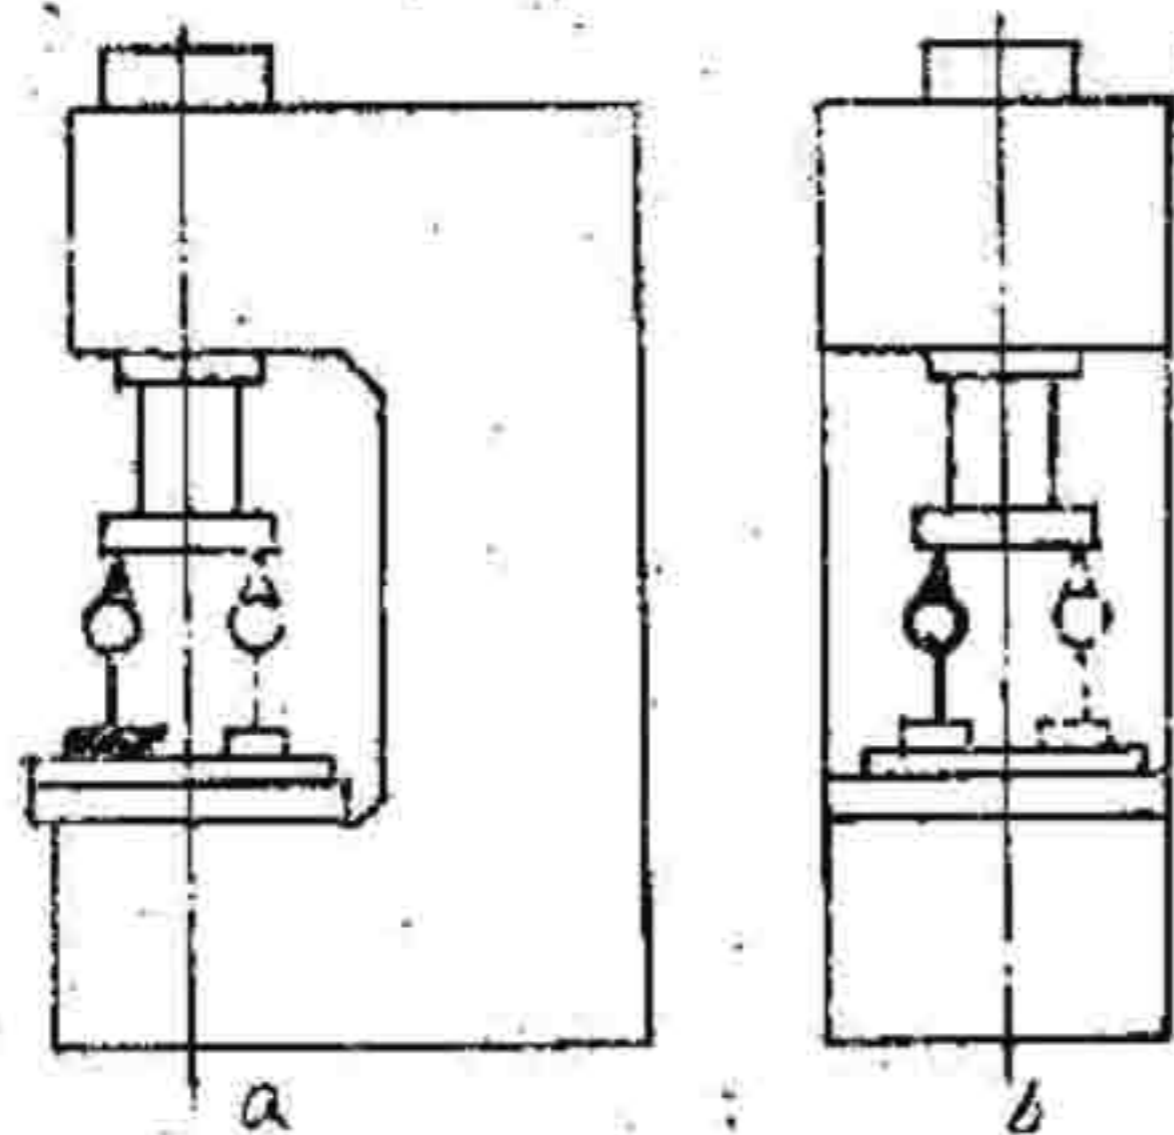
检验滑块（活塞杆）下平面与工作台上平面的平行度
